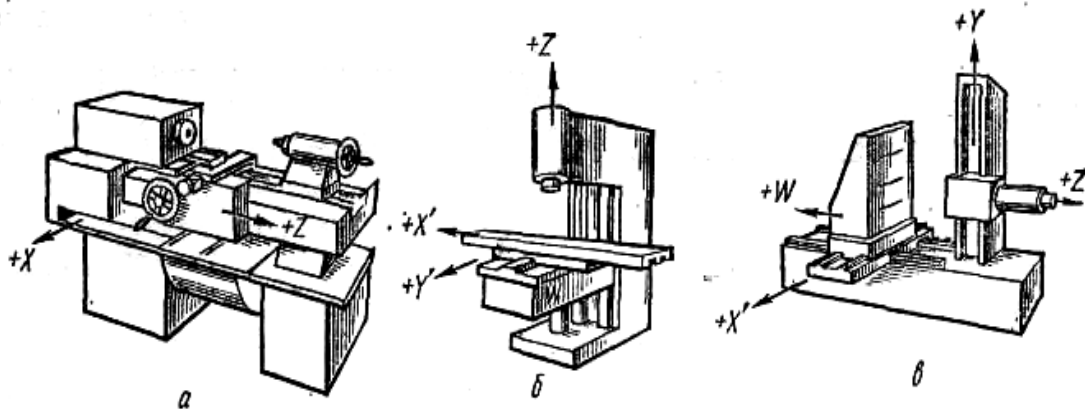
Примеры расположения осей координат на станках с ЧПУ:
